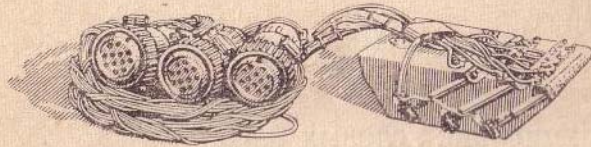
Экспериментальный щуп для контроля сварных соединений методом «бегающего» луча.
